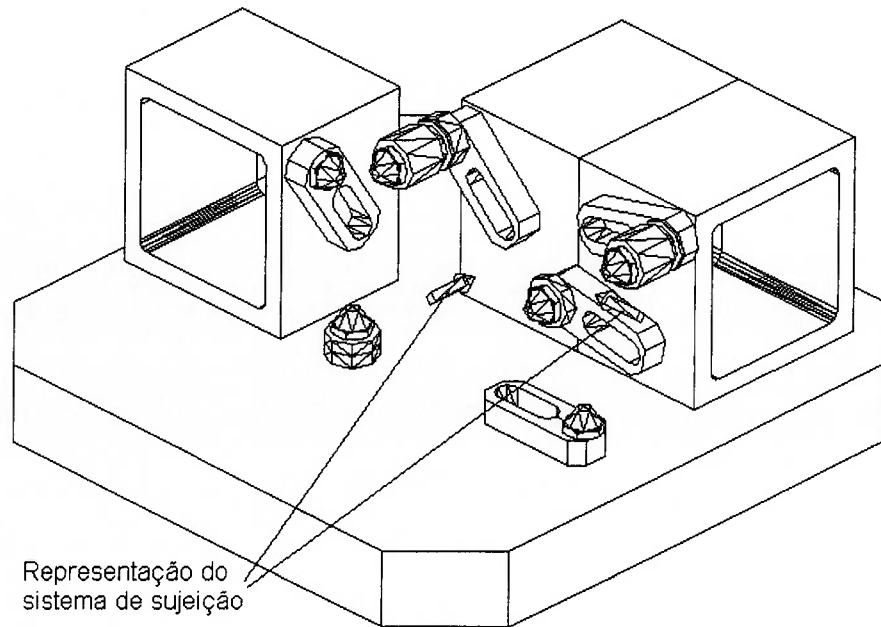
Montagem do dispositivo para usinagem de F1, sem representação do produto.
